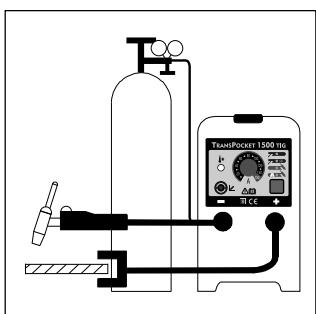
TP 1500 в оснащении для сварки ТИГ
